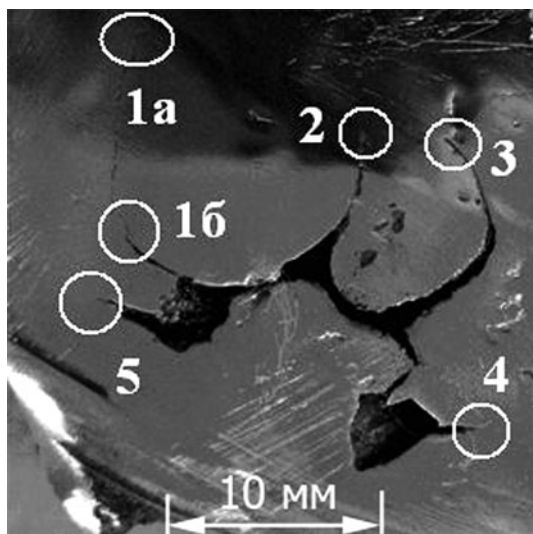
Поверхность с трещинами и дефектами сварки
